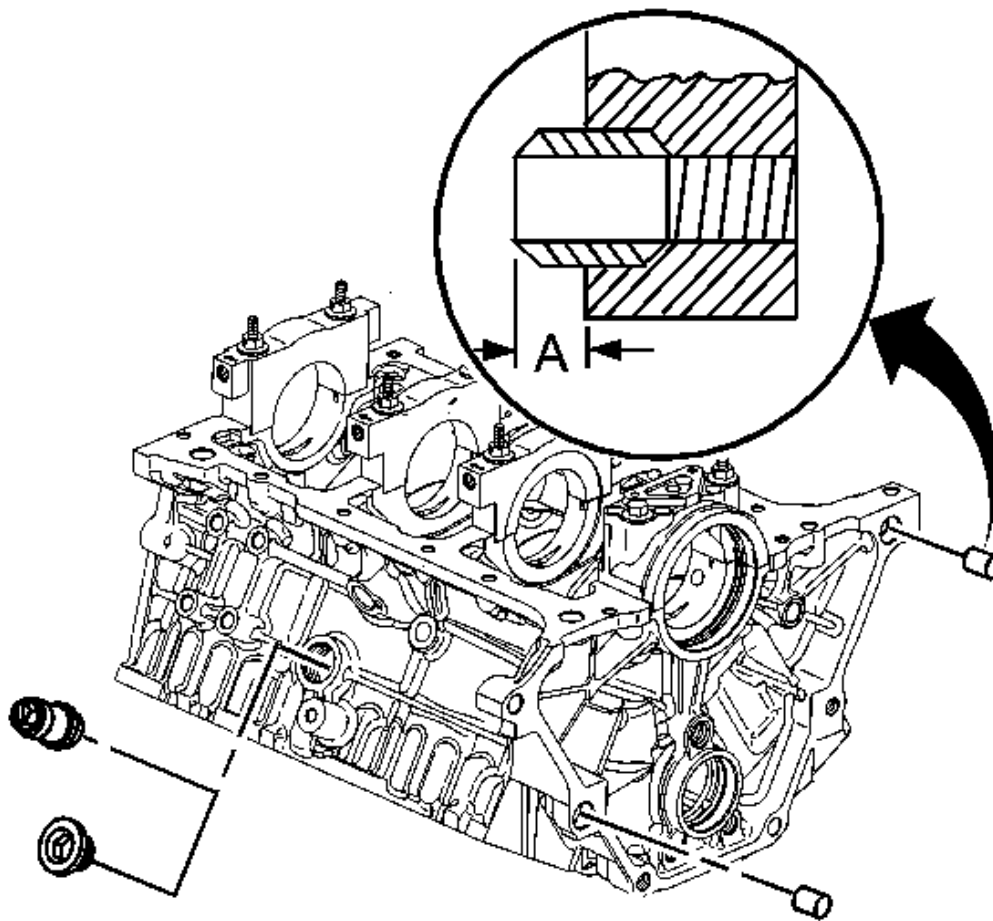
Vista del tapón del bloque del motor, el calentador del bloque del motor y los pasadores de ubicación de la transmisión
